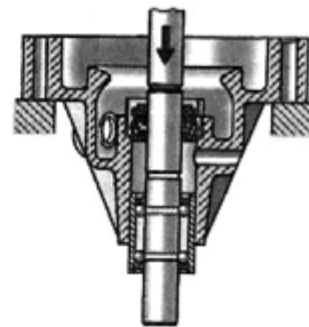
Выпрессовка подшипника с валиком водяного насоса
